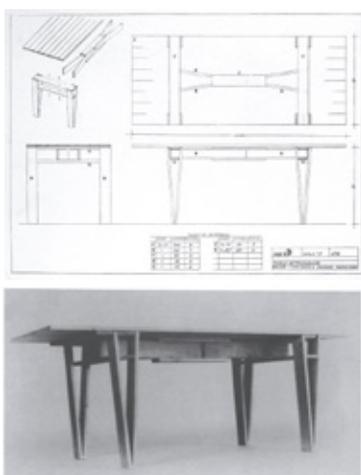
ENZO MARI, Autoprogettazione, Tavolo rettangolare, plan, 1974.
